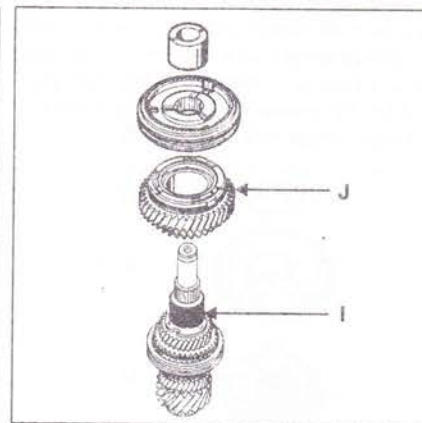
Установите игольчатый подшипник I, шестерню 2-й передачи J с установленными кольцами синхронизатора с тремя конусами.
